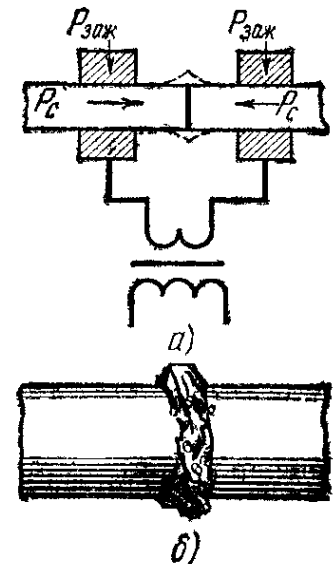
Схема стыковой сварки (а) и сварной стык (б)
